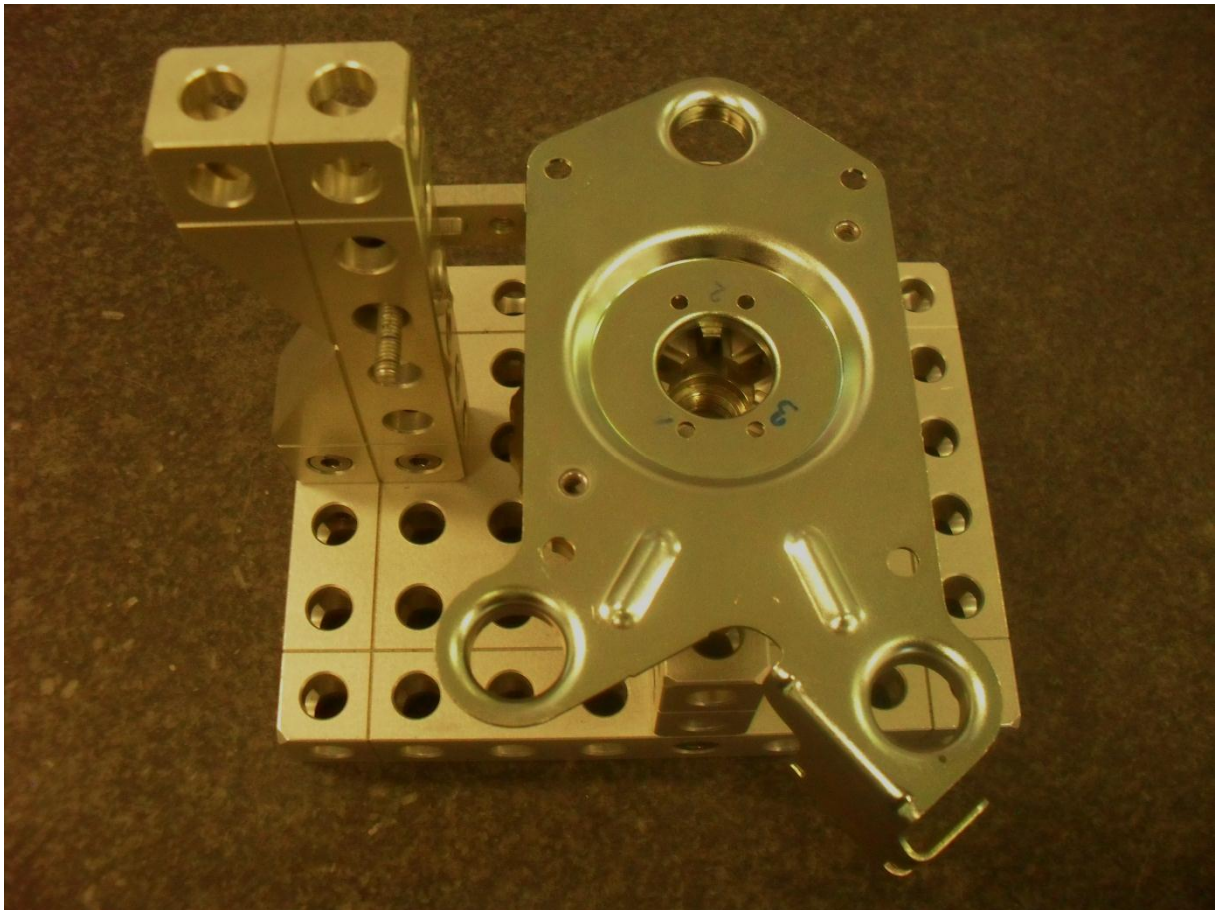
upevněný díl na přípravku při měření dotykem (\varnothing 2 mm)
